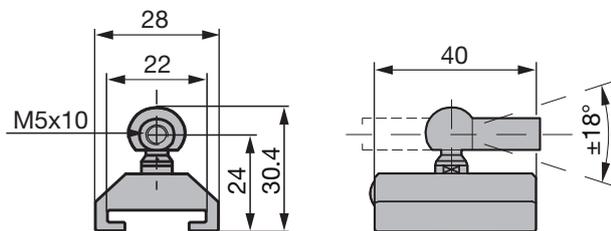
BTL5-F-2814-1S 磁环安装尺寸
